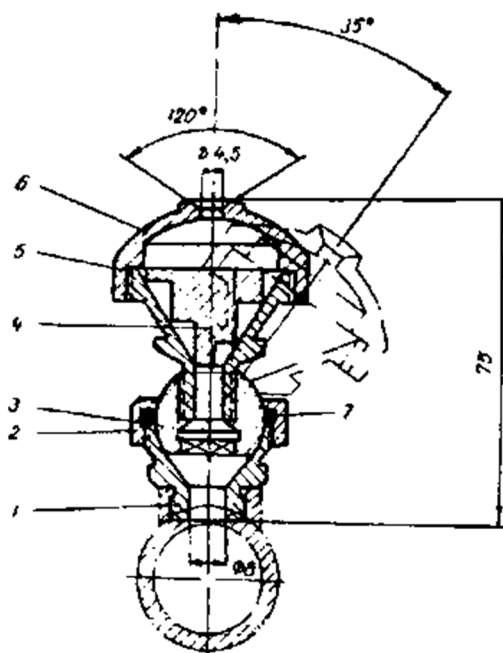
Форсунка прямоточна шарнірна:
